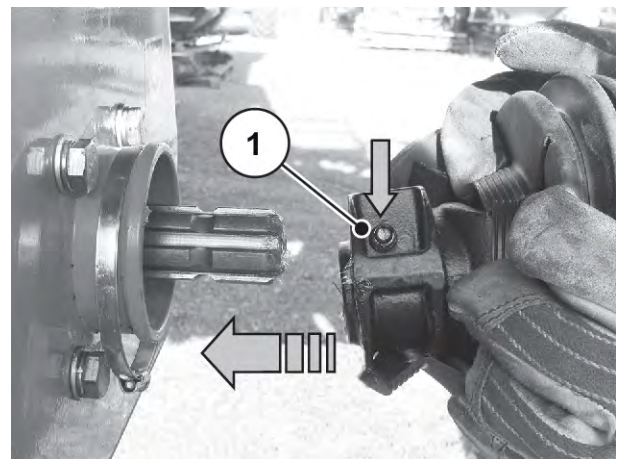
Montage de l'arbre de transmission sur l'axe de l'engrenage
